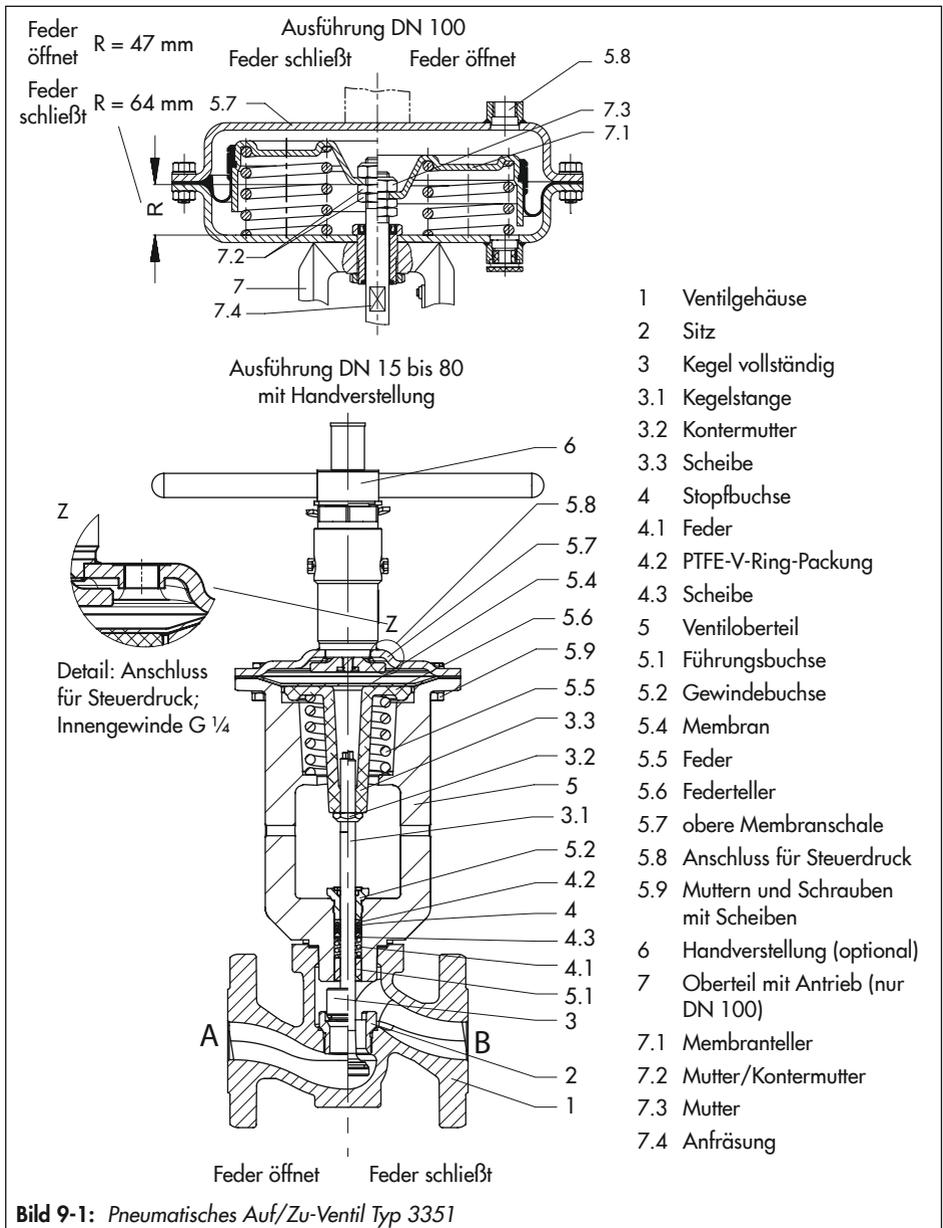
Pneumatisches Auf/Zu-Ventil Typ 3351
